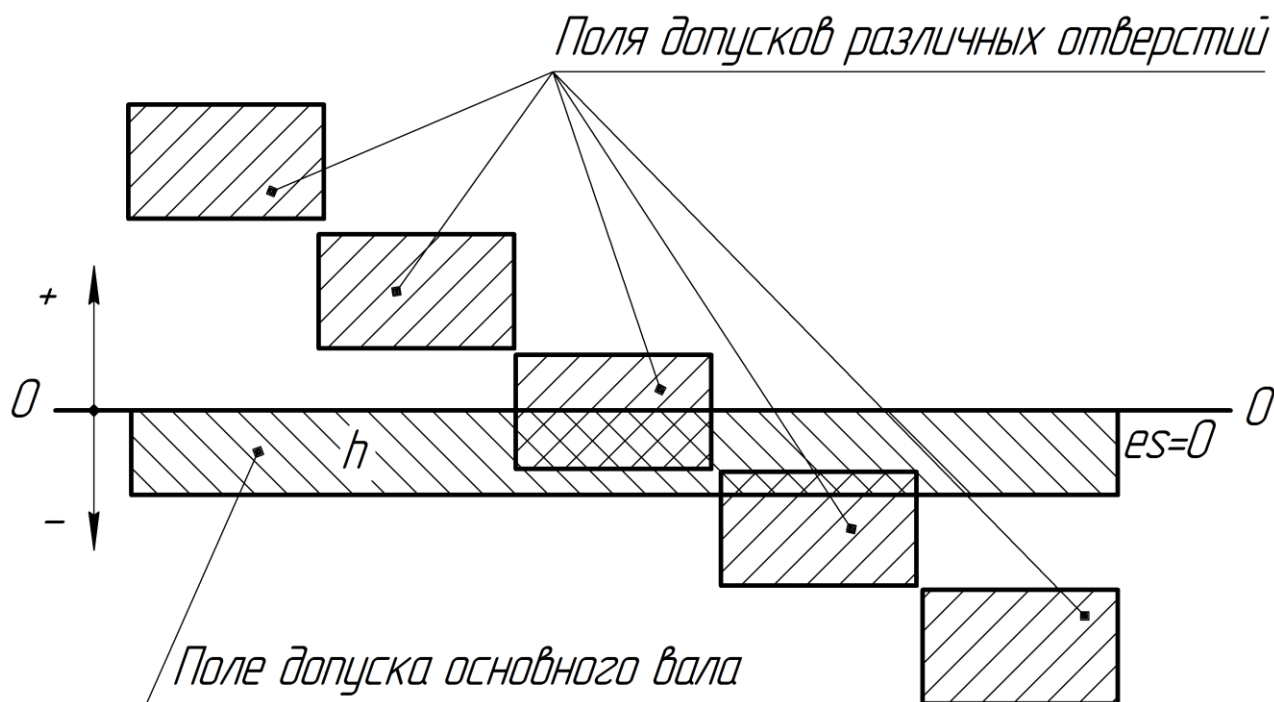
Схема расположения полей допусков в системе вала
